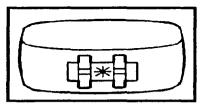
del catálogo 3M Unitek. Soldado de un solo punto
